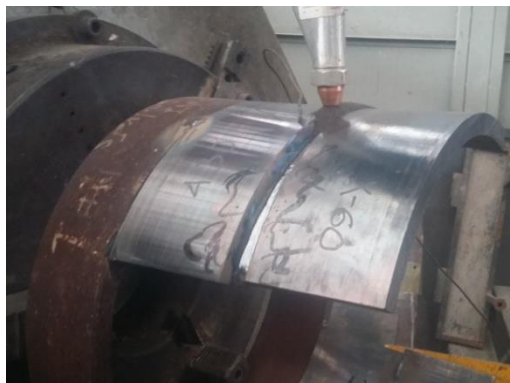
Montaje de las placas para pruebas de soldaduras.
